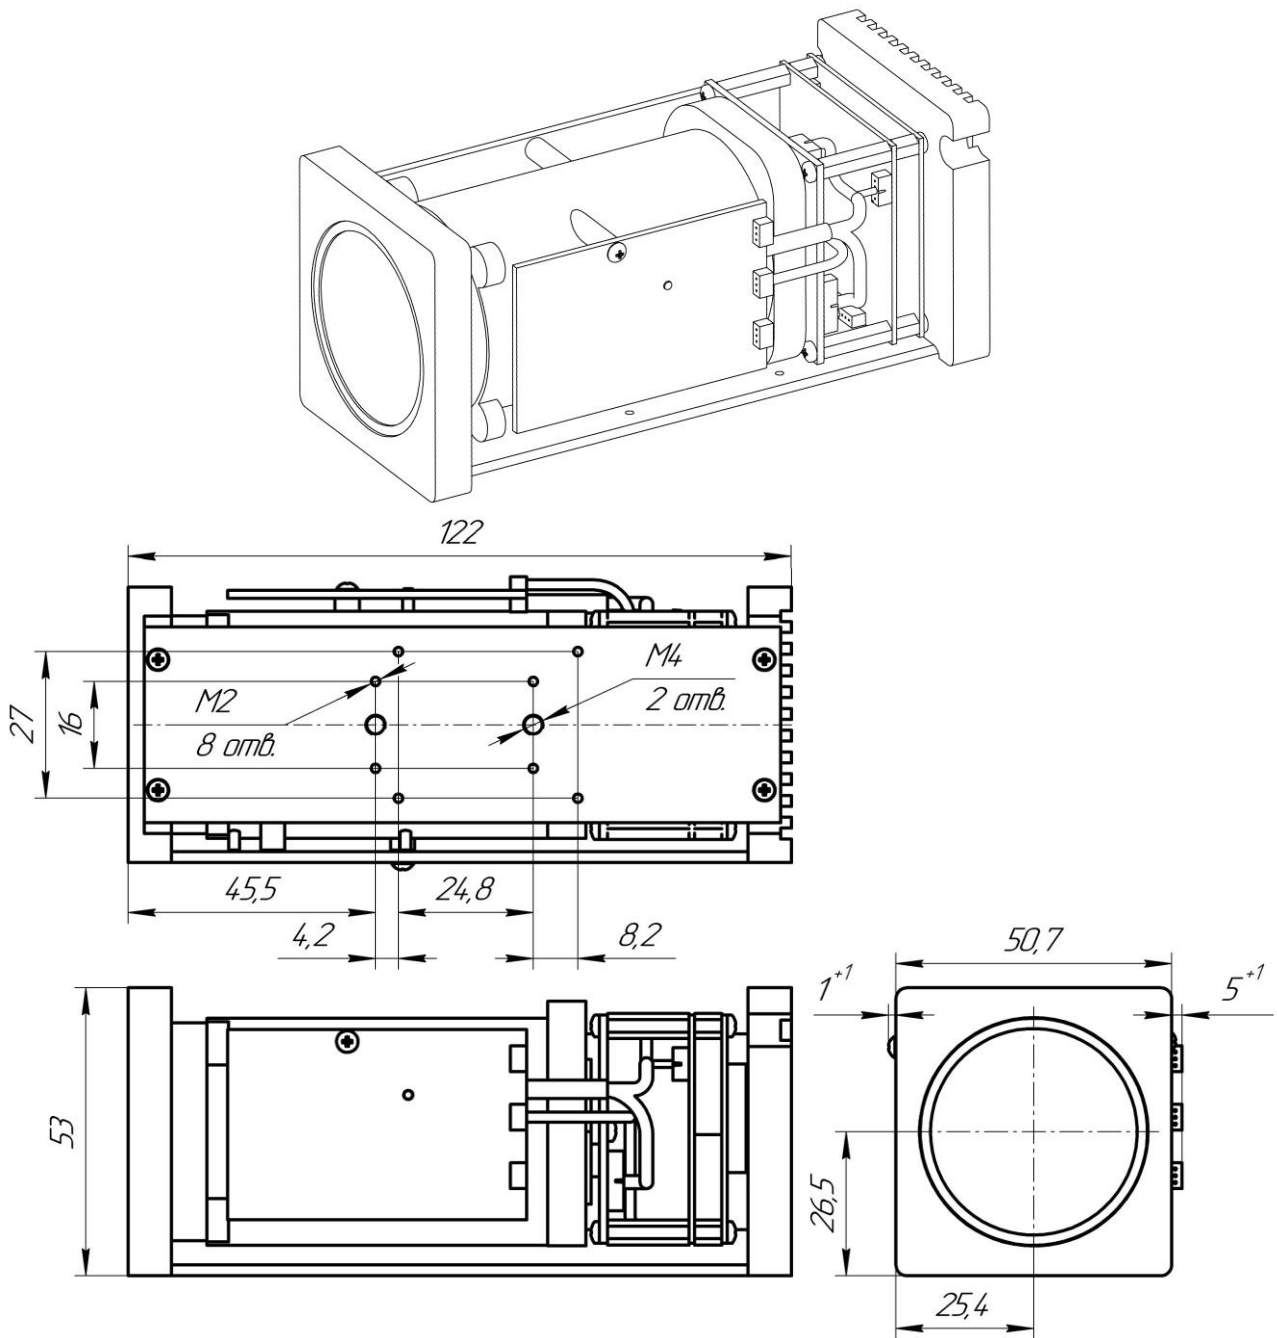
Габаритные и установочные размеры камеры ВНЗ-1030V2W
